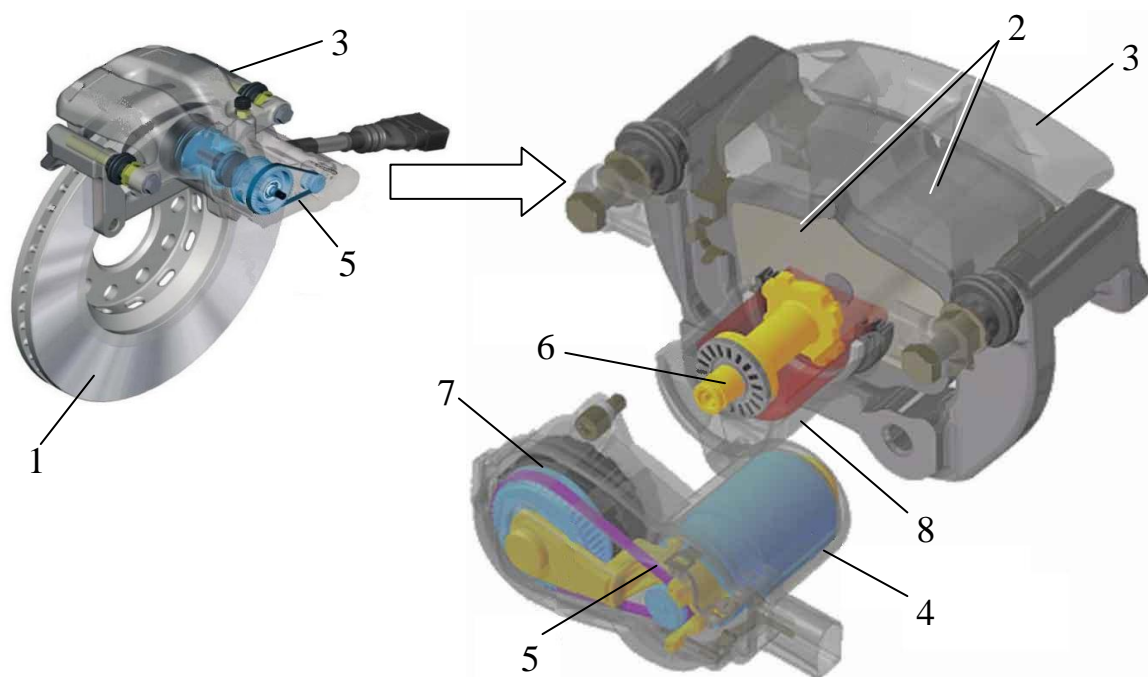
Привод электромеханического стояночного тормоза с редуктором и ременной передачей: 1 – тормозной диск; 2 – тормозные колодки; 3 – суппорт тормозного механизма; 4 – электродвигатель; 5 – зубчатый ремень; 6 – винтовая пара; 7 – редуктор; 8 – поршень рабочей тормозной системы
